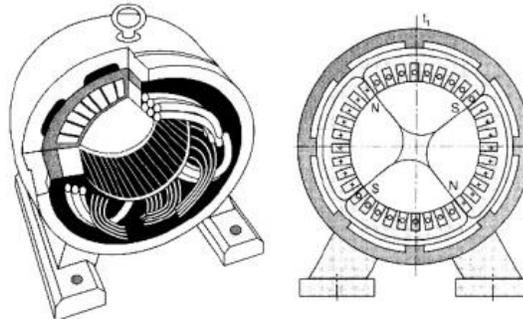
Motor de rotor bobinado con anillos rasantes
